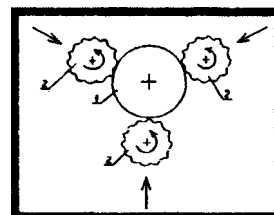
Схема холодного накатывания мелко модульного зубчатого колеса:
